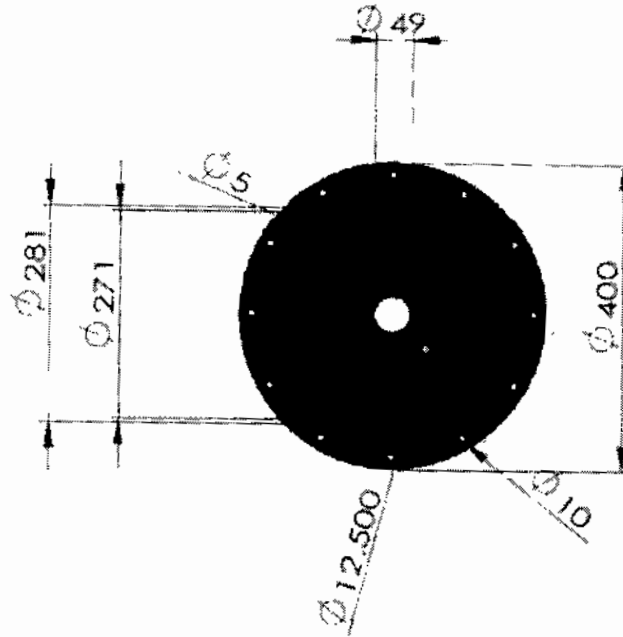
ภาพ drawing ฐานรองชิ้นงาน (แบบยาว)
